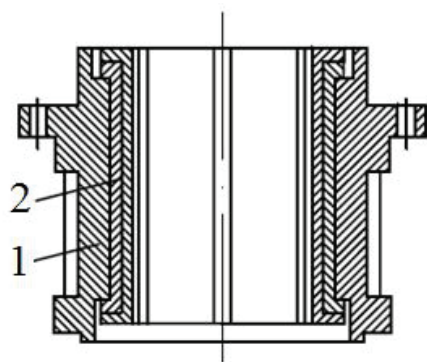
Схема направляющего подшипника насоса с обрезиненными вкладышами:
